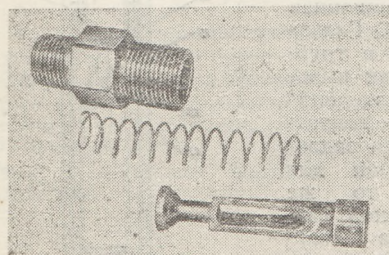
Детали полуавтоматического клапана: 1 — корпус; 2 — пружина; 3 — клапан
